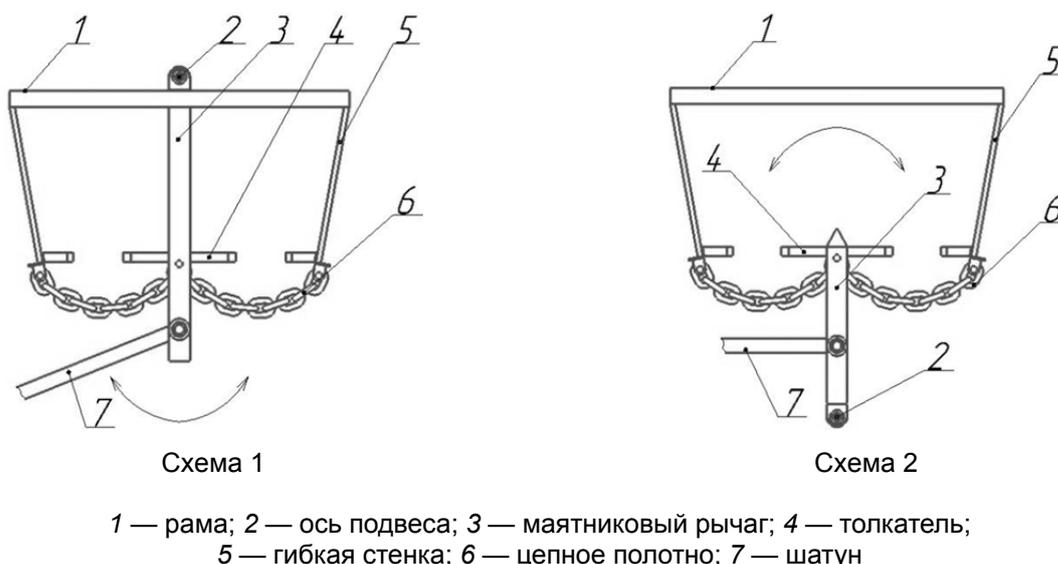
Варианты схем цепного агрегата с волновой рабочей камерой
